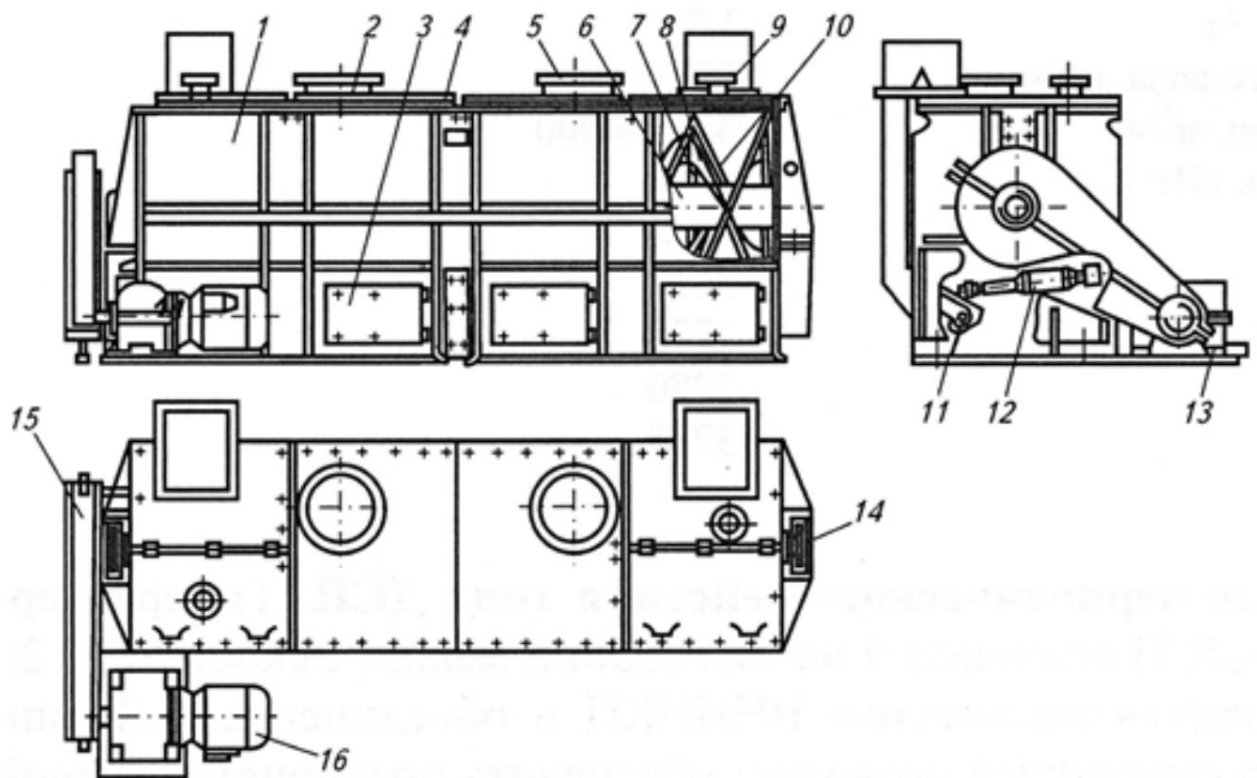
Змішувач А9-БСГ-3: 1 - корпус; 2, 5 - завантажувальні патрубки; 3 - люк; 4 - кришка; 6 - лопатевий вал; 7 - стійка; 8, 10 - спіральні лопаті; 9 - патрубок; 11 - ступка; 12 - пневмоциліндр; 13 - плита; 14 - підшипник; 15 - ланцюгова передача; 16 - мотор-редуктор
